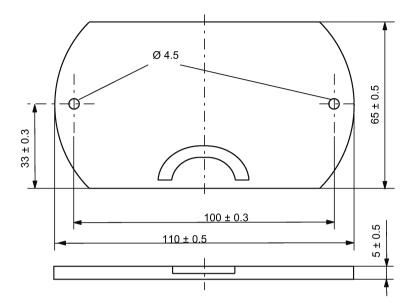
Desenho de dimensões da bolsa de fixação 6GT2390-0AA00
